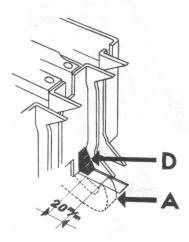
Réglage de l'arrêt de piston 20 mm = 0.8 in.
